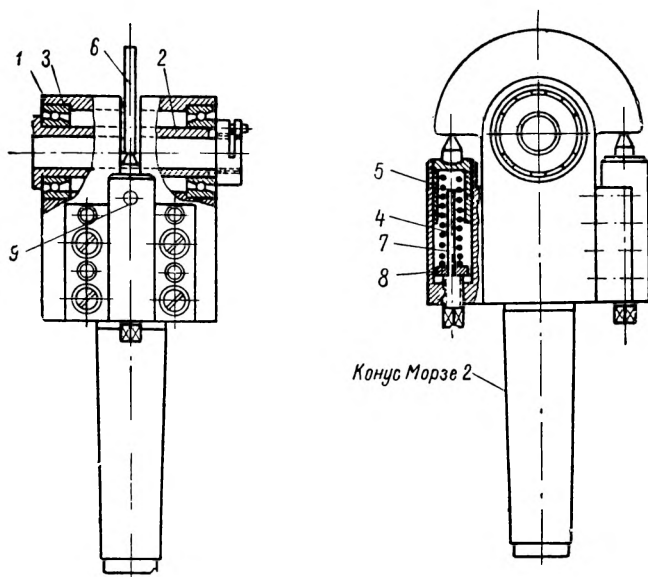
Универсальный держатель для расточного и резьбонарезного инструмента.
